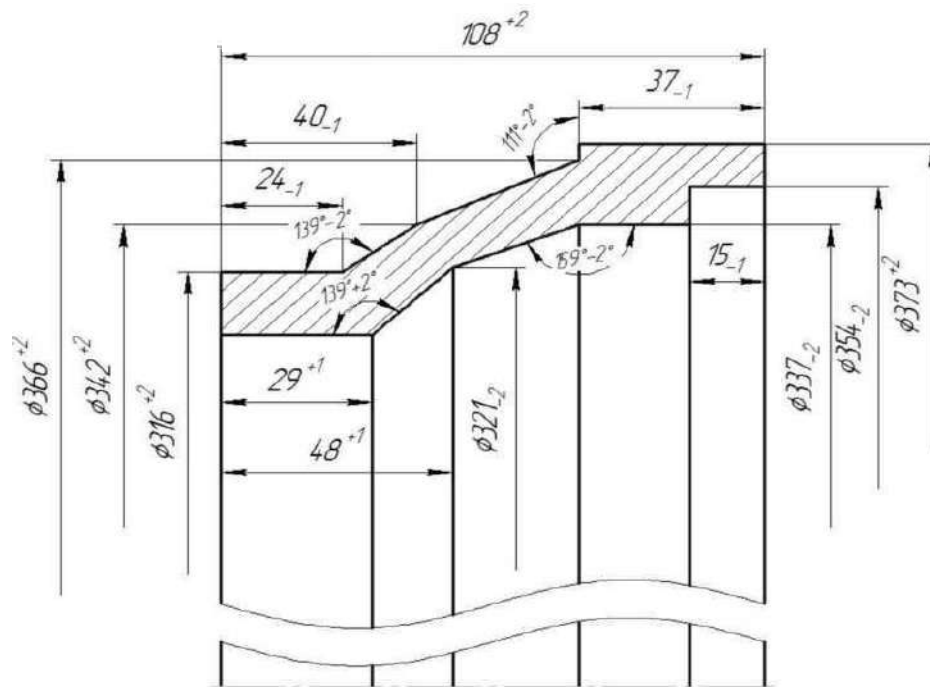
креслення заготовки кільця зовнішнього жарового груби під вирощування методом мікроплазмового порошкового наплавлення
